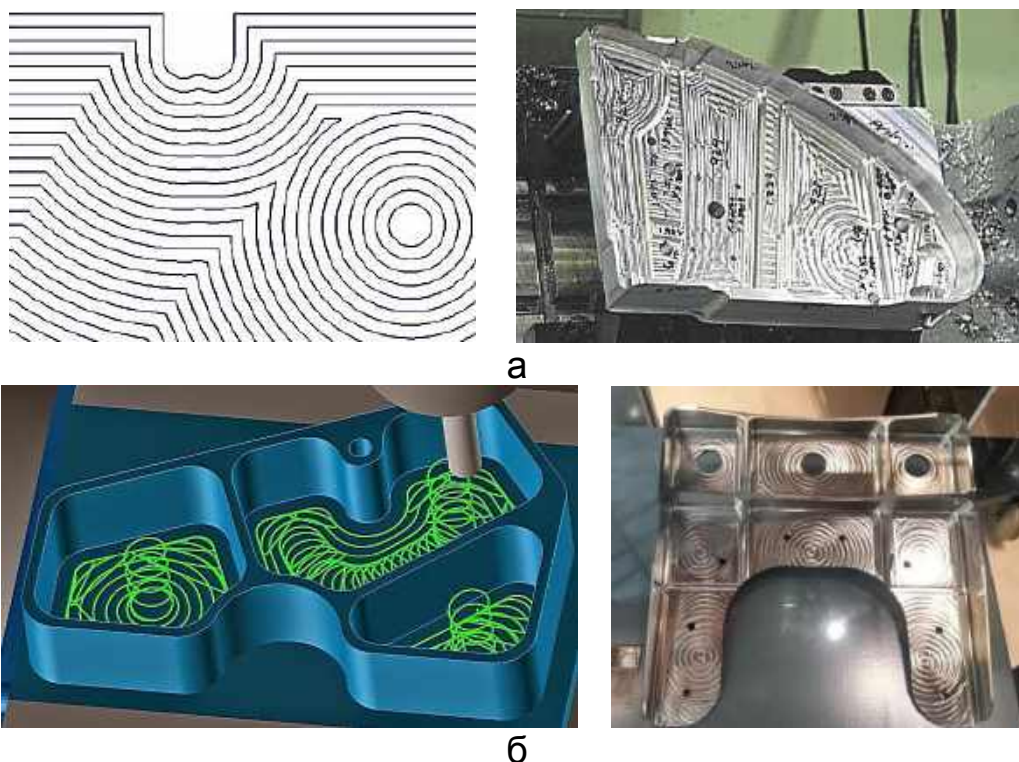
Приклади траєкторій для фрезерної обробки:
